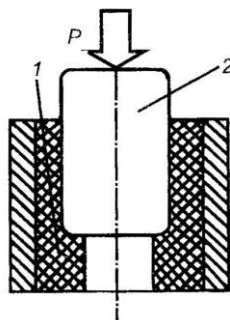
Восстановление размеров детали калиброванием: 1 — полимерное покрытие; 2 — калибр
